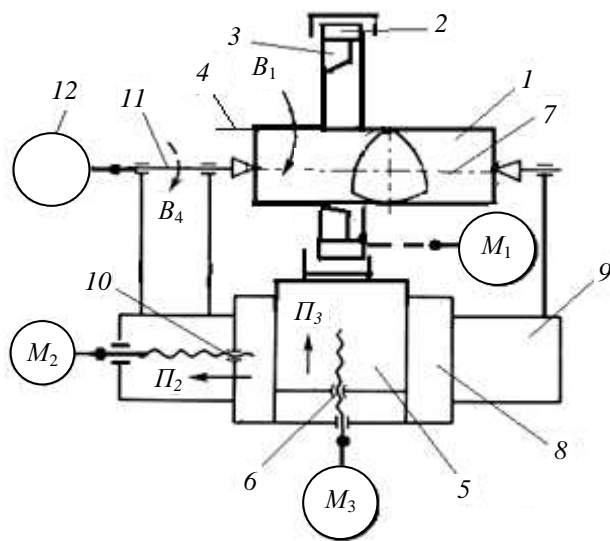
Структурная схема станка для обработки круговым точением деталей с профилем в виде треугольника Рело
